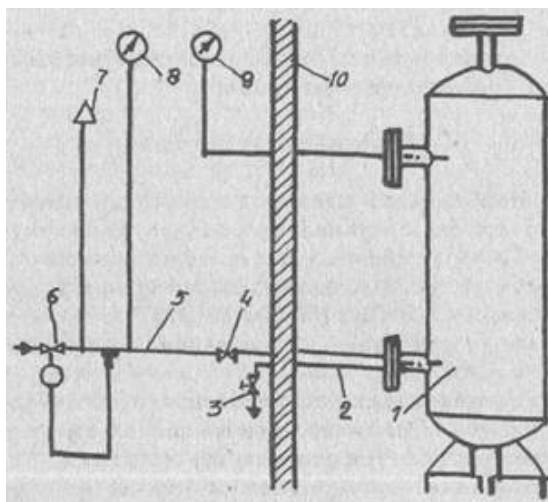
Принципиальная схема пневматического испытания сосудов (аппаратов): 1 - испытываемый сосуд; 2 - трубопровод сброса воздуха; 3 - запорный вентиль сброса воздуха; 4 - запорный вентиль подачи воздуха; 5 - трубопровод подачи воздуха; 6 - редукционный клапан; 7 - предохранительный клапан; 8 - манометр рабочий; 9 - манометр контрольный; 10 - стена здания
